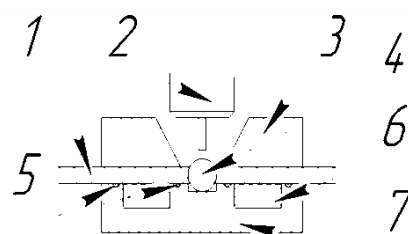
Пример устройства омывающего изделие водой: 1 – свариваемые детали; 2 – сварочная головка; 3 – прижимы; 4 – сварочный шов; 5 – уплотнитель; 6 – охладитель (вода); 7 – корпус
